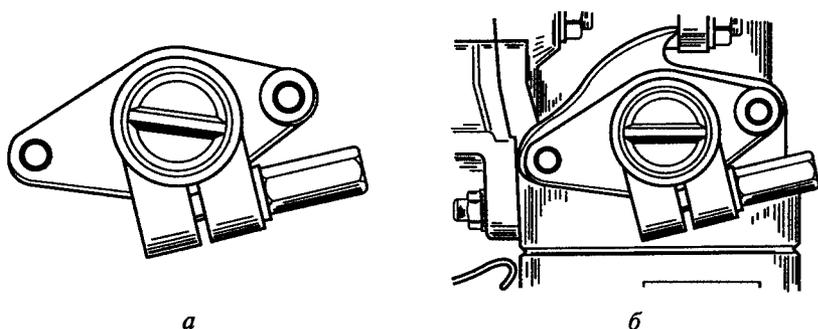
Положение паза на валике привода прерывателя—распределителя зажигания:
